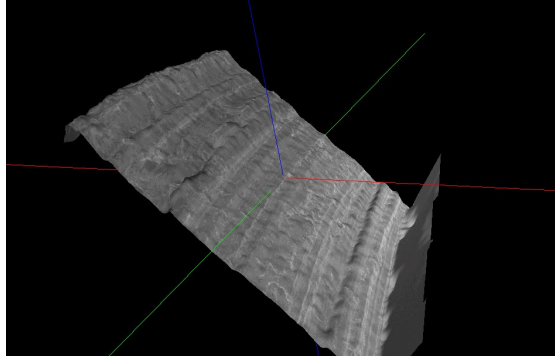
3D-Ansicht einer Gewindeflanke
